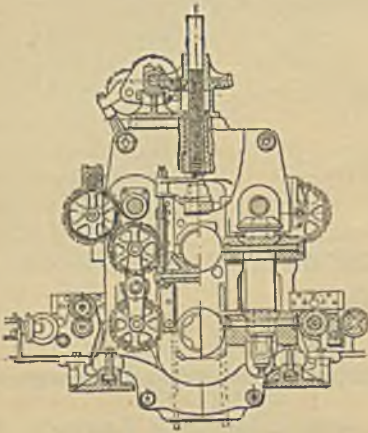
Universalwalzwerk. Grundriss.
